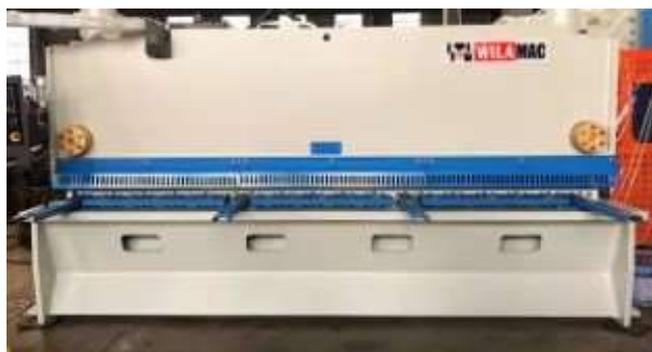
Máquina de corte de tarugo CNC WILA-30 (WILA MACHINE TOOLS, 2024).
